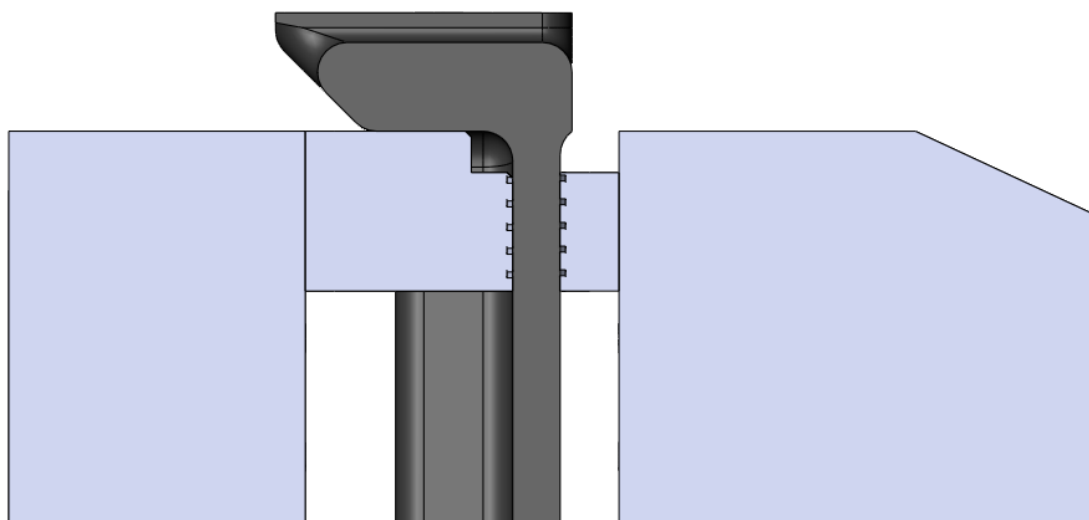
Закріплення заготовки в пневмолещатах
